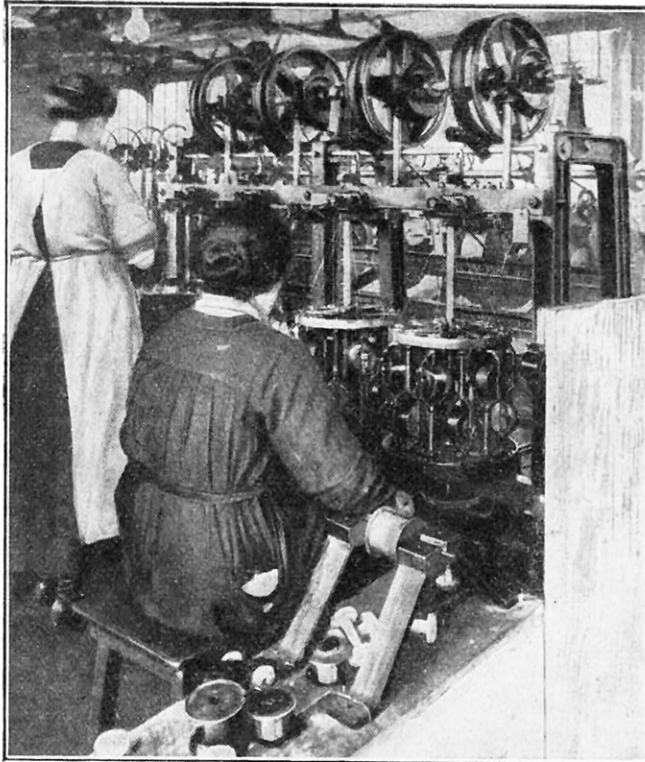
PETITE CABLEUSE A DÉTORSION POUR FABRIQUER DES CABLES TRÈS SOUPLES A FILS EXTRÊMEMENT FINS
